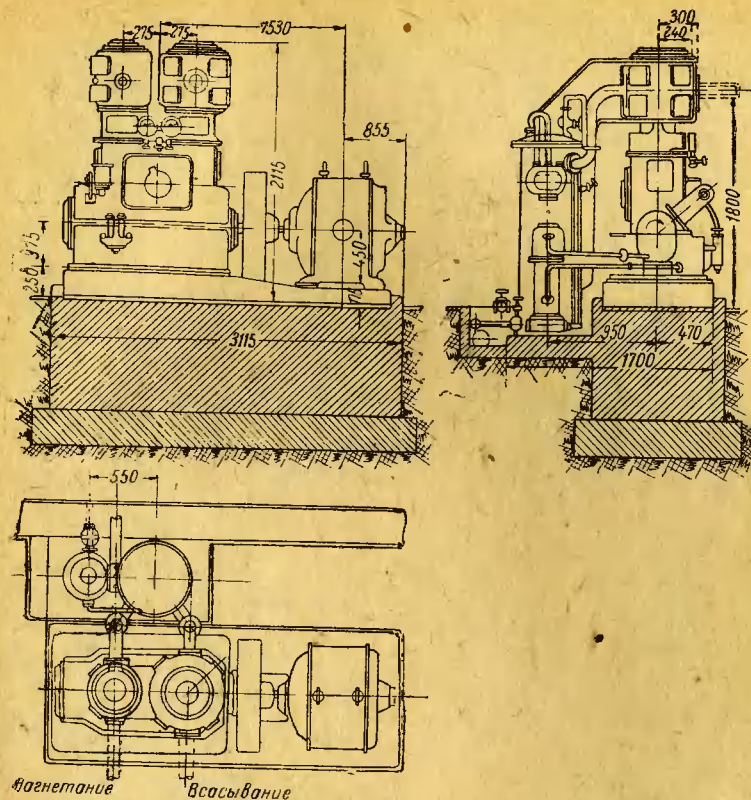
Вертикальный двухцилиндровый воздушный компрессор марки СА-8 завода „Борец“
